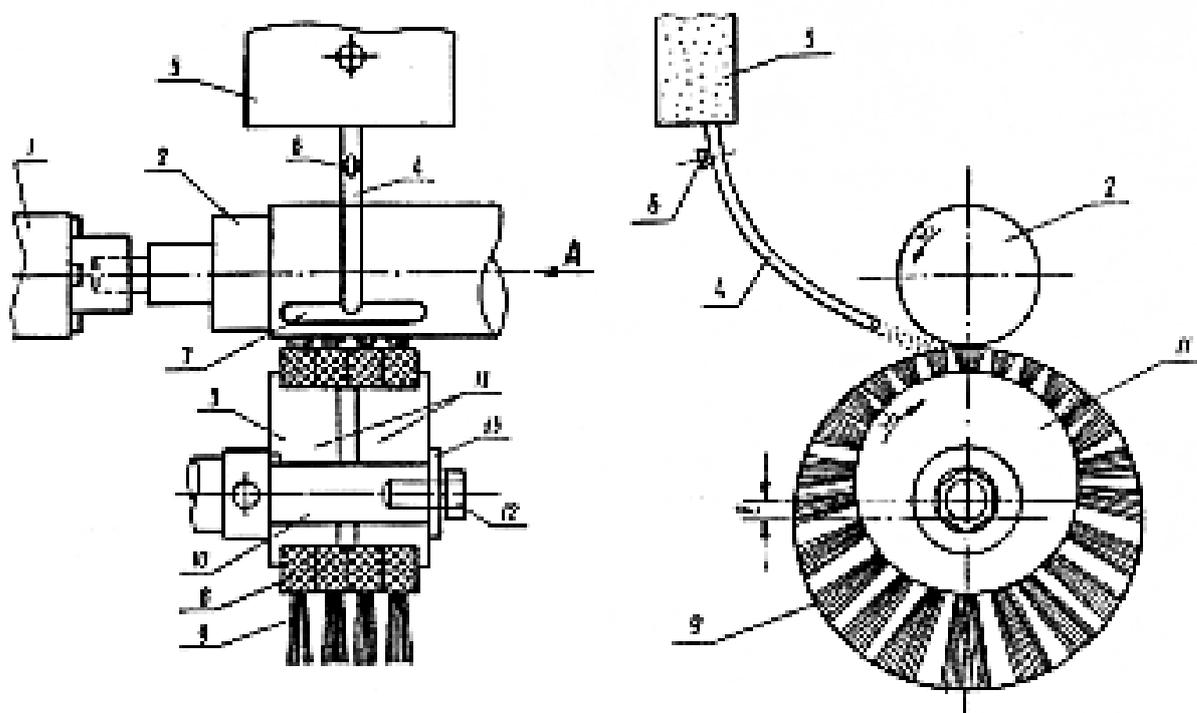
Устройство для осуществления способа притирки деталей ротационной щеткой (вид сбоку)
